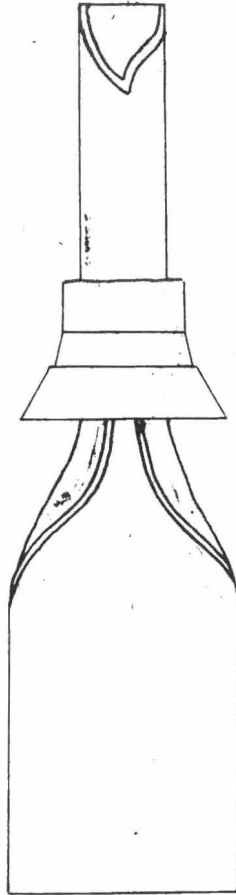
TUBERIA SOLDADA "WELDED BELL".
